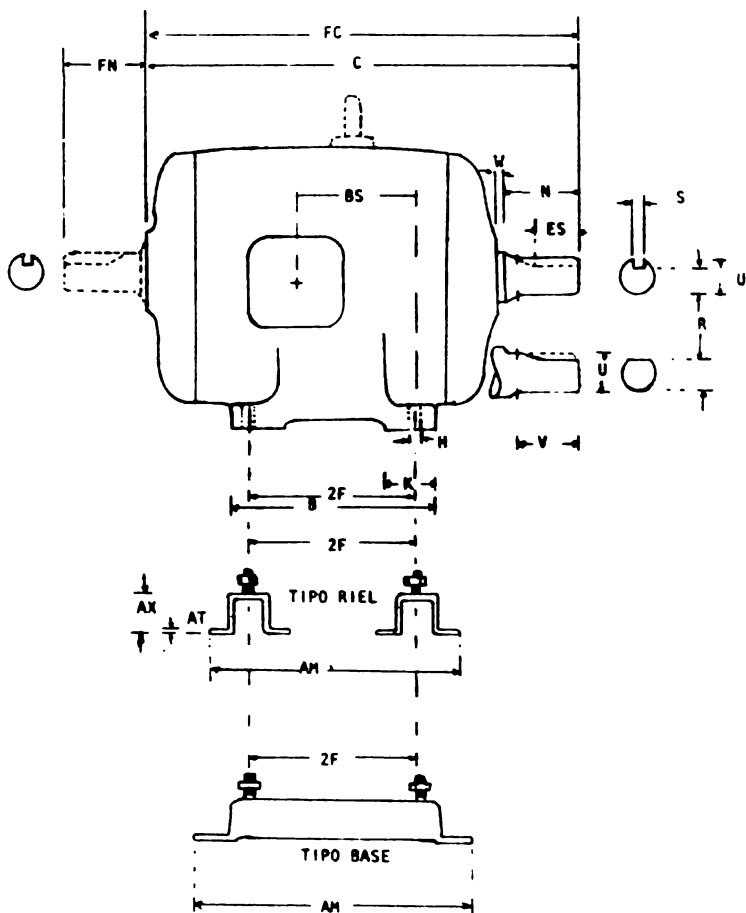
2 DIMENSIONAMIENTO POR LETRAS PARA MAQUINAS MONTADAS AL PISO, VISTA LATERAL.
